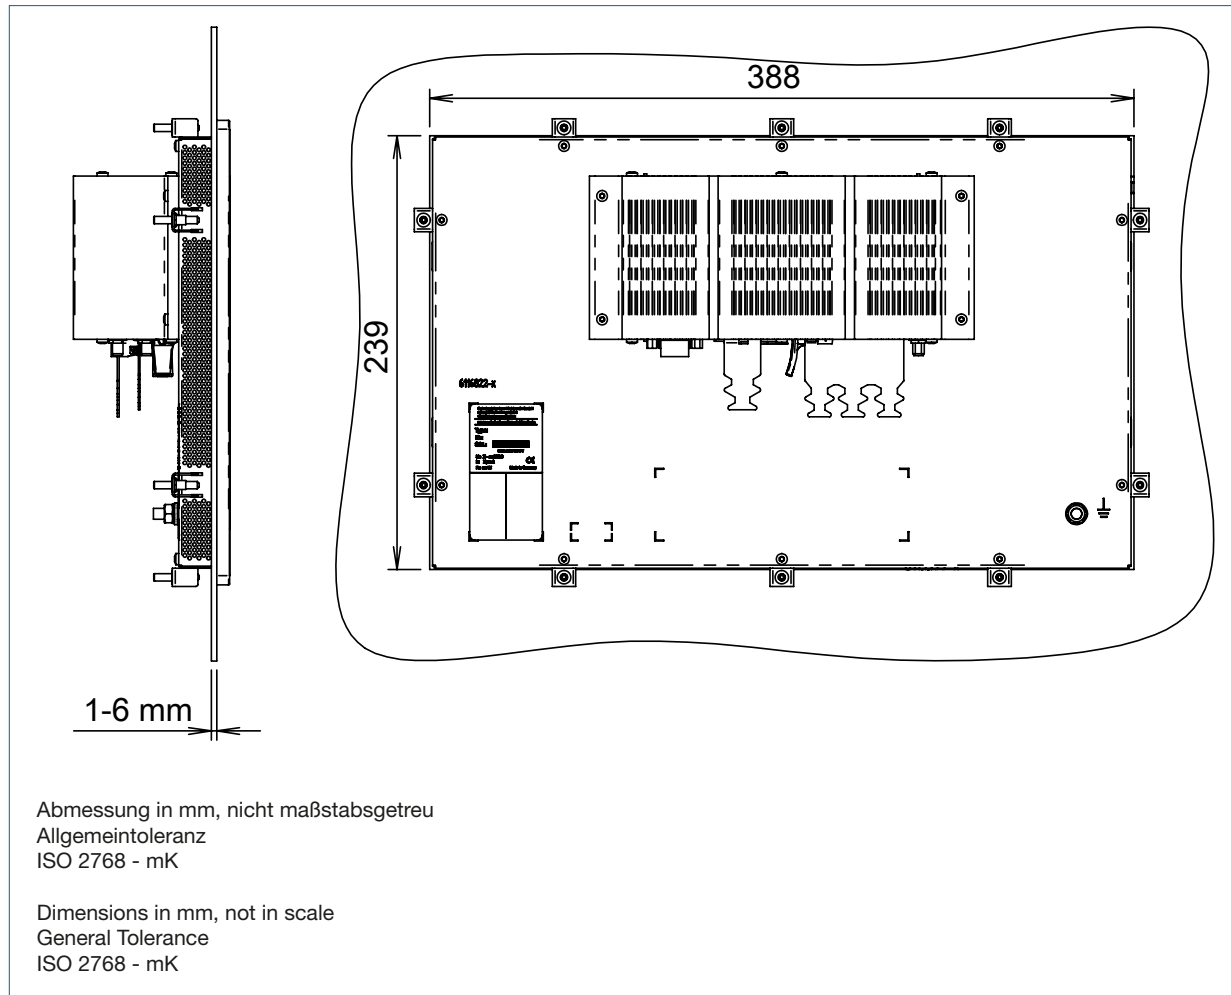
15,6" Prime Panel Pico Einbau - Einbauausschnitt
